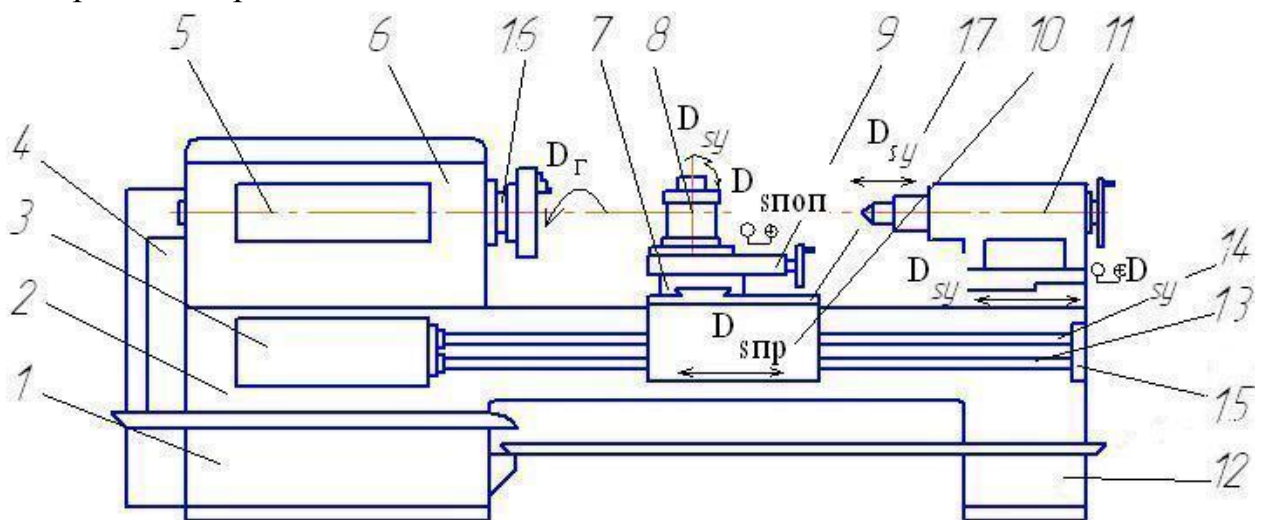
Устройство токарно-винторезного станка модели 16к20
